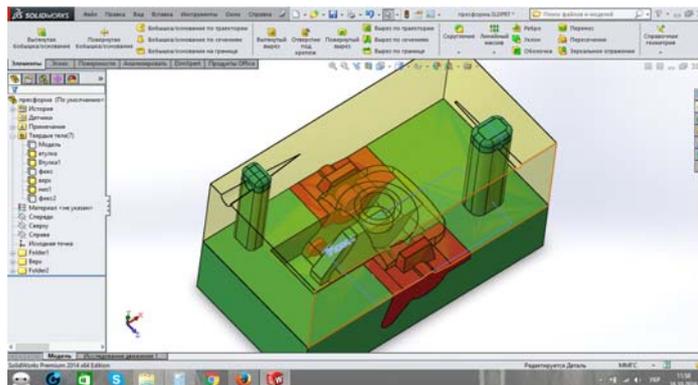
3D-пресс-форма лиття восковок в сборе
